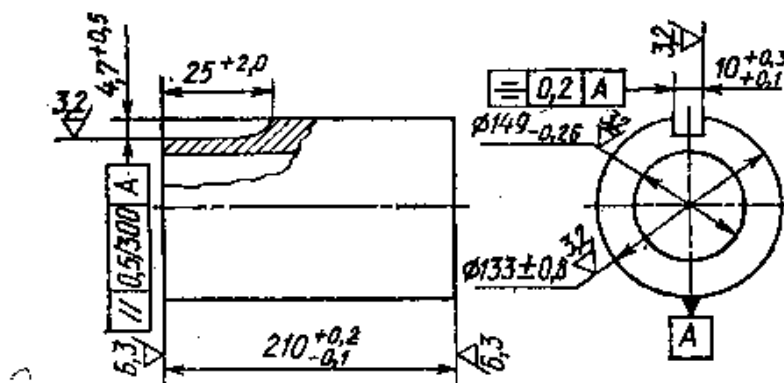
Чертеж заготовки корпуса стартера после выполнения операции фрезерования паза.
